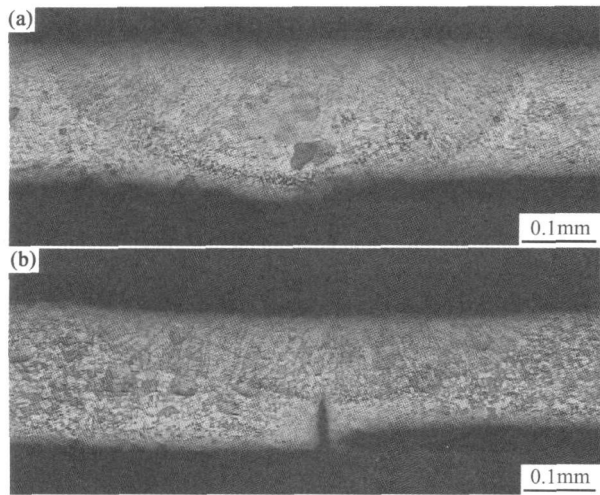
焊接接头的横截面形貌 (a) 成形良好; (b) 未焊透
